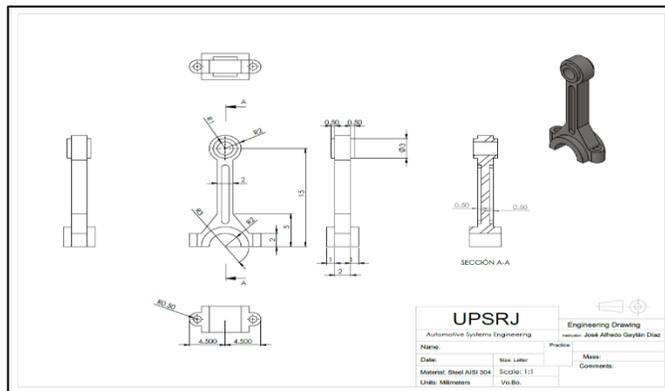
Plano con vistas solicitadas al practicante. Fuente: Diseño propio.
